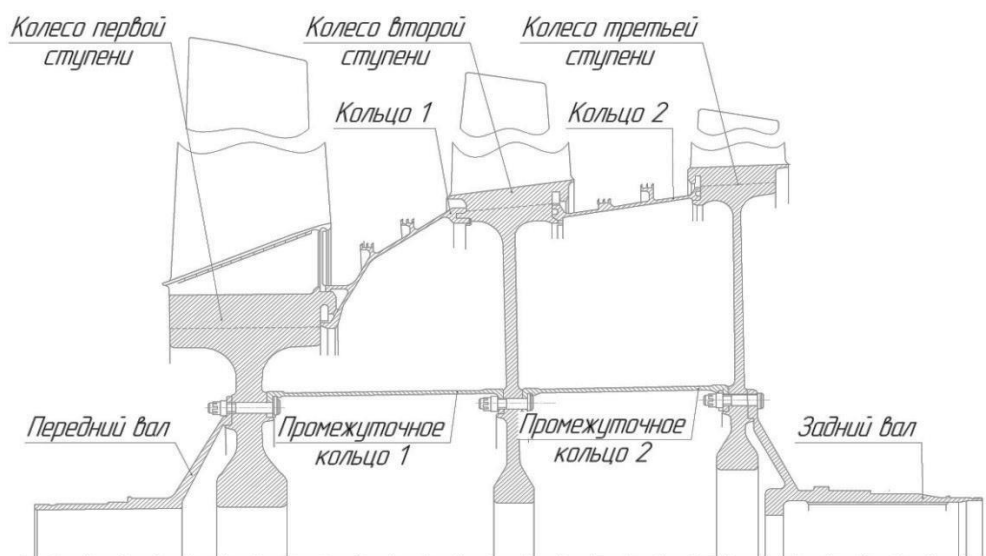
Эскиз ротора компрессора низкого давления
